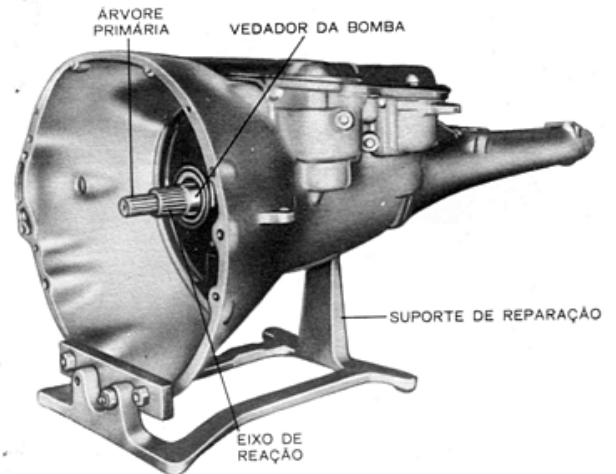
Transmissão instalada sobre o suporte de reparação
